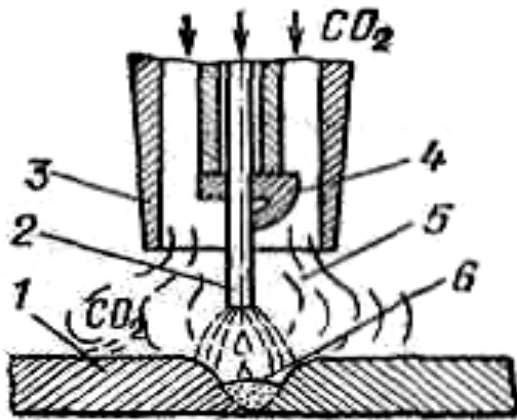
Схема дугового зварювання в середовищі вуглекислого газу: 1-зварювані деталі; 2- електродна проволока; 3- газове сопло; 4- башмак, плідючий струм; 5- захисний шар газу; 6 – наплавлений метал блиску кромки і прилегли до них поверхні труб (приблизно 10 мм від крайки)
